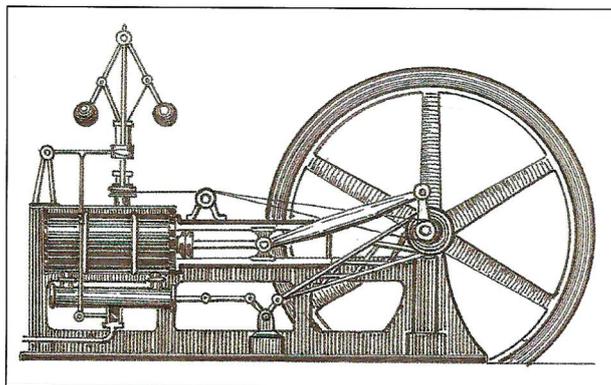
La machine de Watt, dessin de Michel Gendraud
